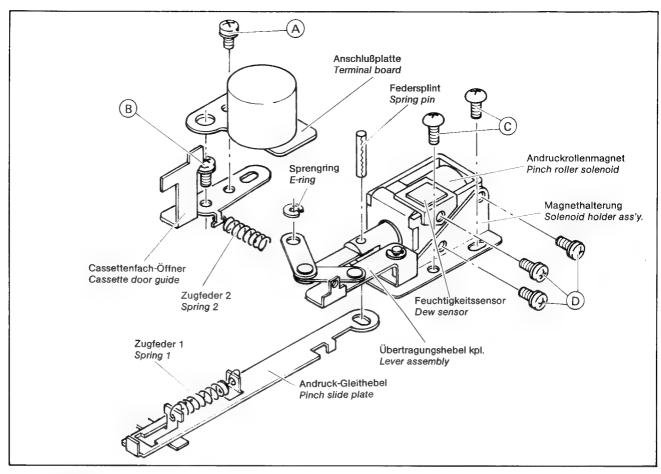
Andruckrollenmagnet-Ausbau Fig. 2-12 Pinch roller solenoid replacement
